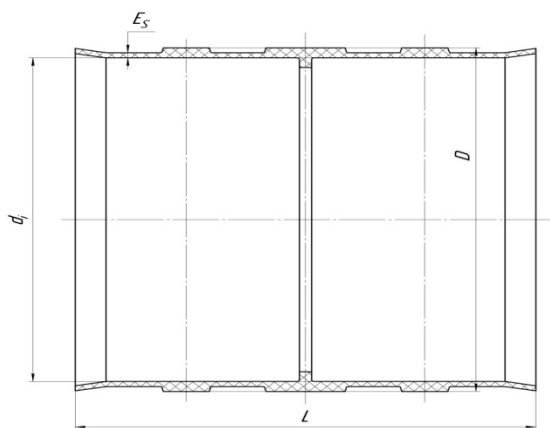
Полиэтиленовая муфта для соединения Труб ПЕРФОКОР равного диаметра (1-й тип)
